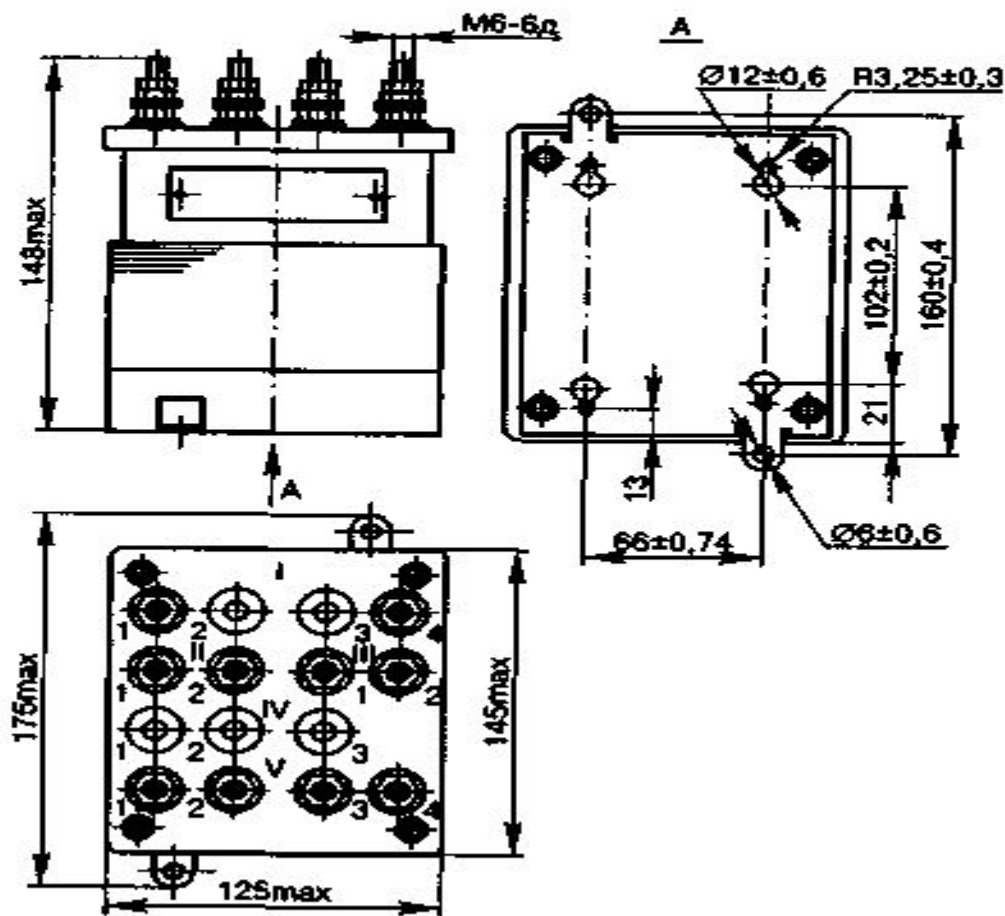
Присоединительные и габаритные размеры трансформатора СОБС-2М
